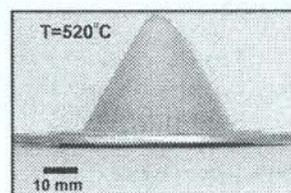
Образец сплава 1570, полученный сверхпластической формовкой из листовой заготовки
